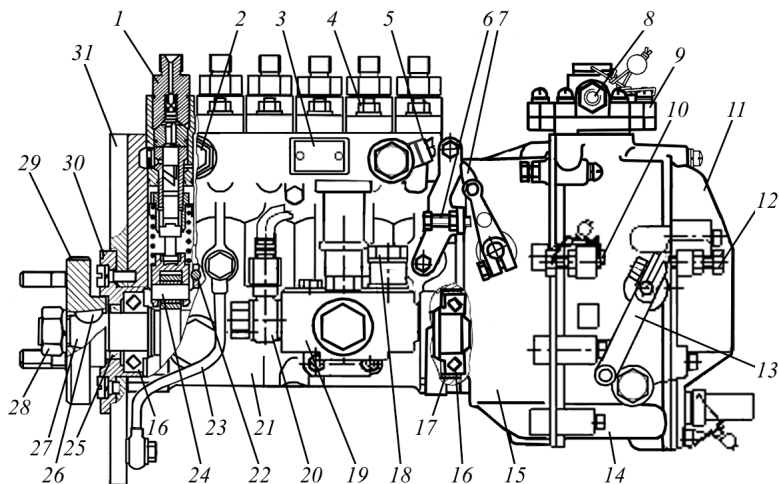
Рядный топливный насос высокого давления: 1 – секция топливного насоса; 2 – перепускной клапан; 3 – табличка; 4 – гайка крепления секции топливного насоса; 5 – штуцер подвода топлива; 6 – болт регулировки пусковой подачи; 7 – рычаг останова; 8 – болт крепления штуцера подвода воздуха; 9 – корректор по наддуву; 10 – болт регулировки максимальной частоты вращения; 11 – крышка смотрового люка; 12 – болт регулировки минимальной частоты вращения; 13 – рычаг управления; 14 – крышка регулятора; 15 – корпус регулятора; 16 – подшипник; 17 – кольцо подшипника; 18 – болт крепления штуцера подвода топлива к подкачивающему насосу; 19 – топливоподкачивающий насос; 20 – штуцер отвода топлива от подкачивающего насоса к фильтру тонкой очистки топлива; 21 – корпус топливного насоса; 22 – направляющий штифт толкателя; 23 – маслопровод; 24 – толкатель; 25 – манжета крышки подшипника; 26 – шпонка; 27 – кулачковый вал; 28 – гайка крепления полумуфты; 29 – полумуфта привода; 30 – крышка подшипника; 31 – установочный фланец
